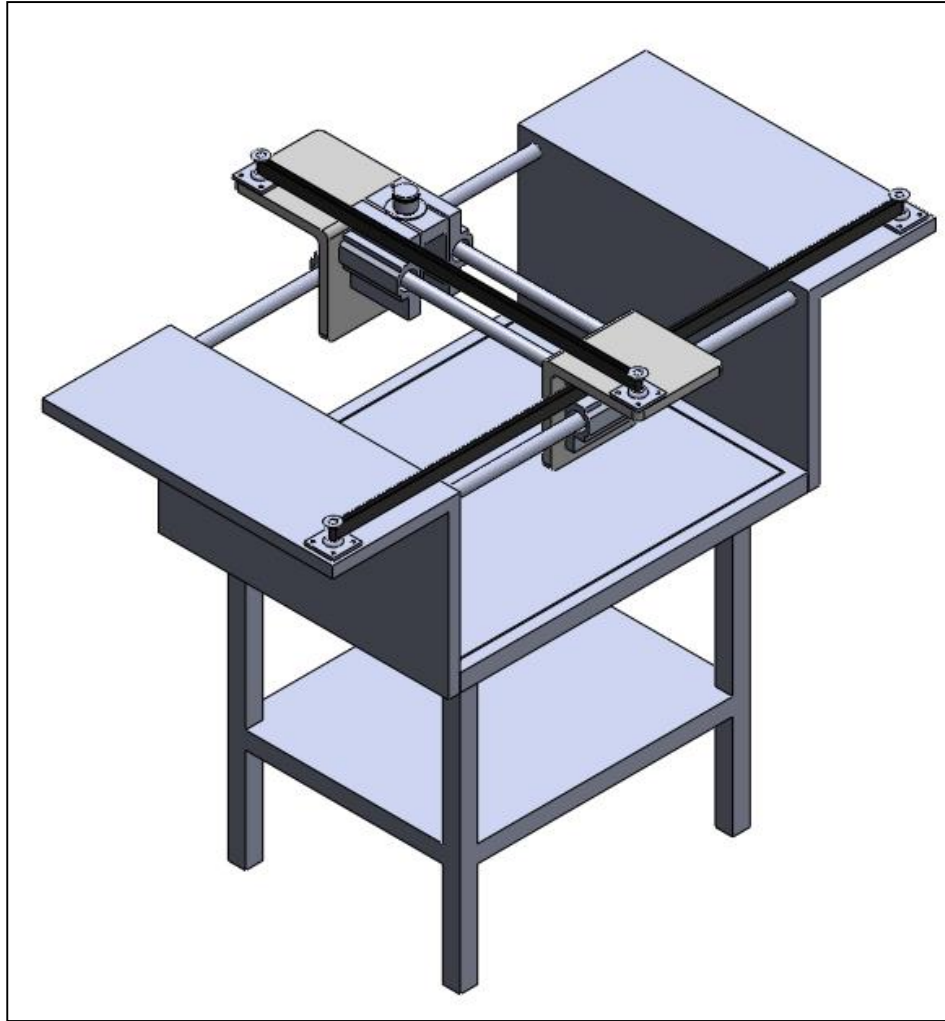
Vista isométrica de la máquina cortadora de vidrio
